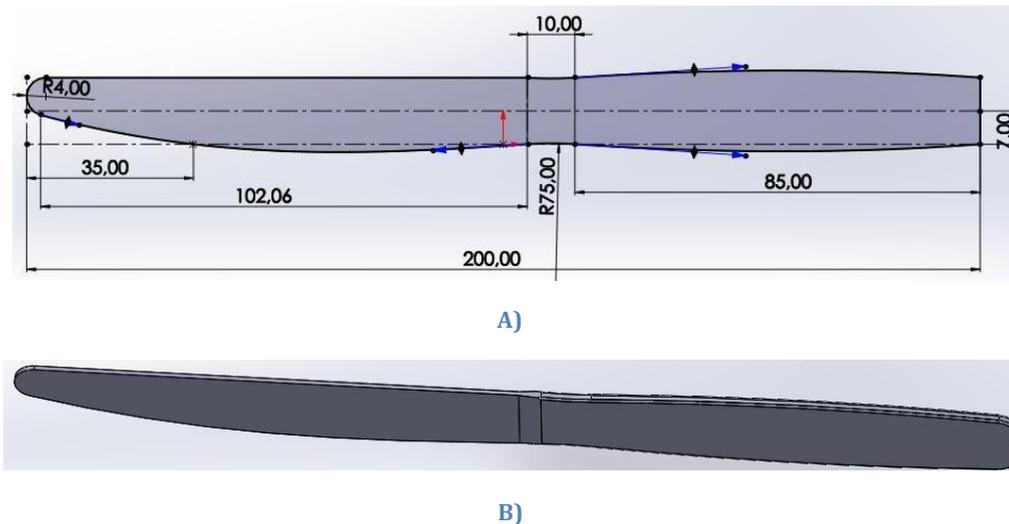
A) Croquis de la forma del cuchillo. B) Dimensiones del cuchillo.
